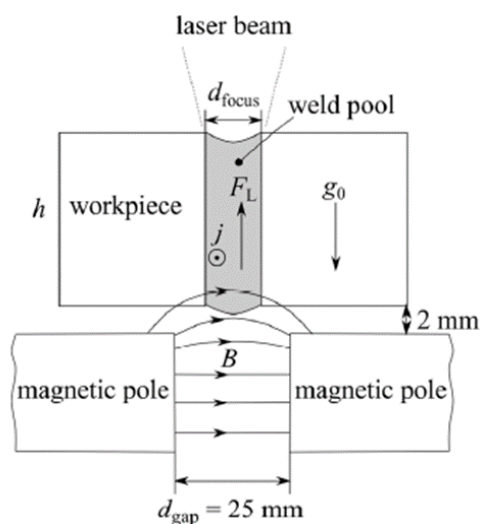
Схема поддержки сварочной ванны на основе силы Лоренца.
